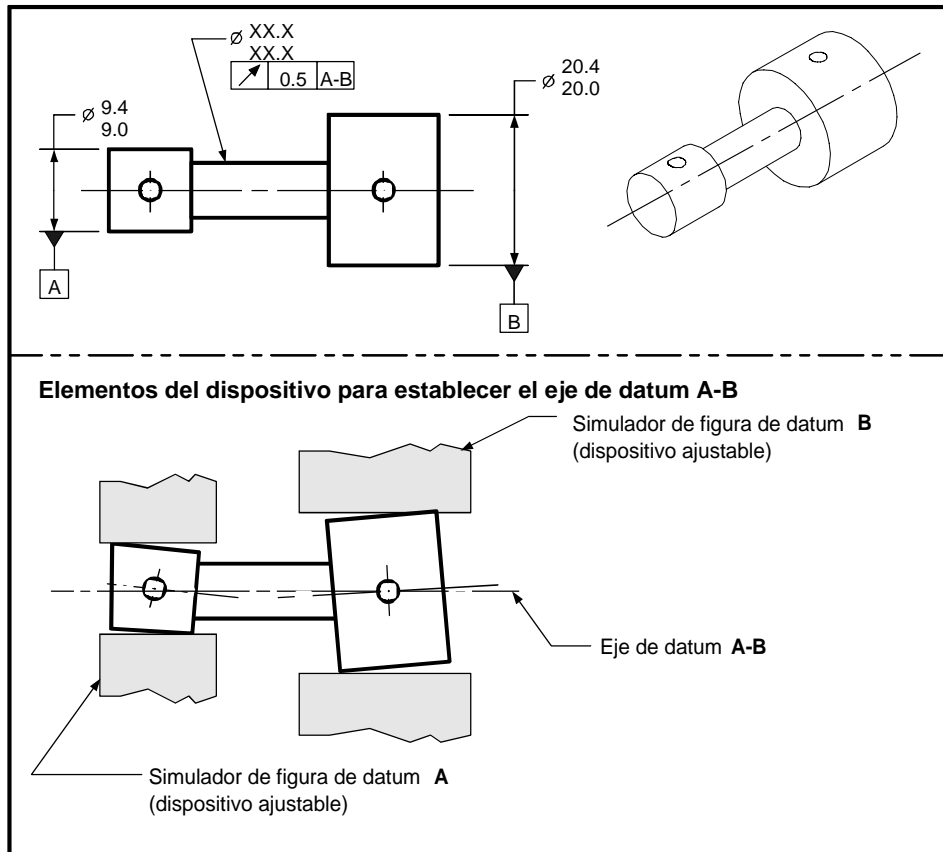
Eje de datum de diámetros coaxiales RFS primario
